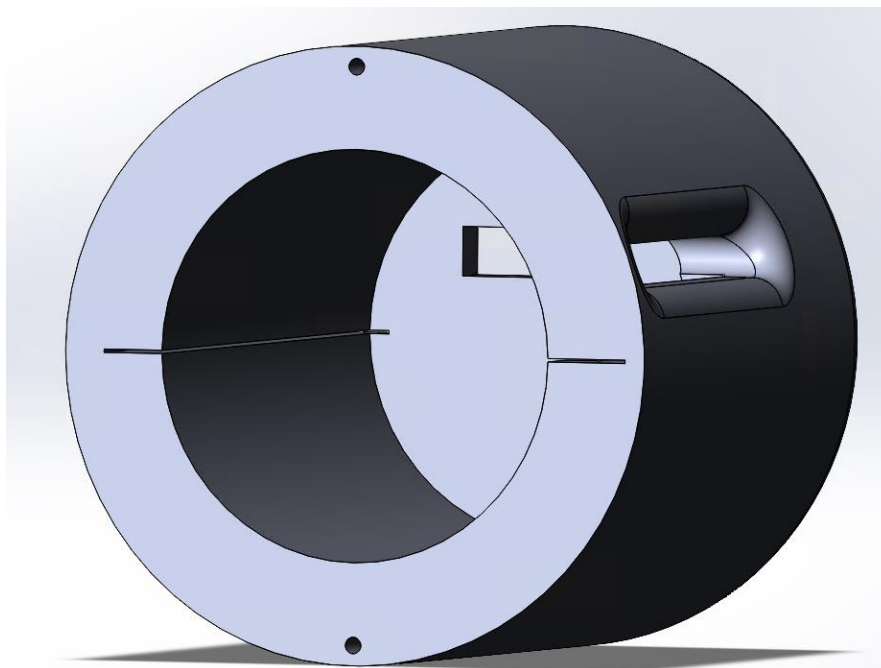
Основна частина корпусу магнітометричного металодетектора
